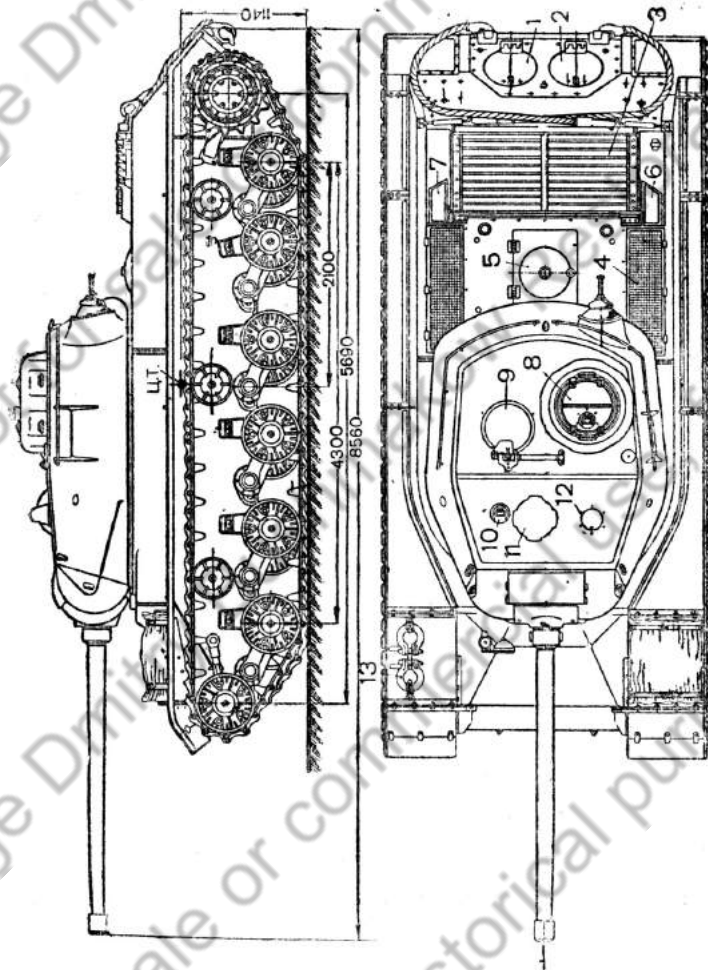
Габаритные размеры и положение центра тяжести танка.
